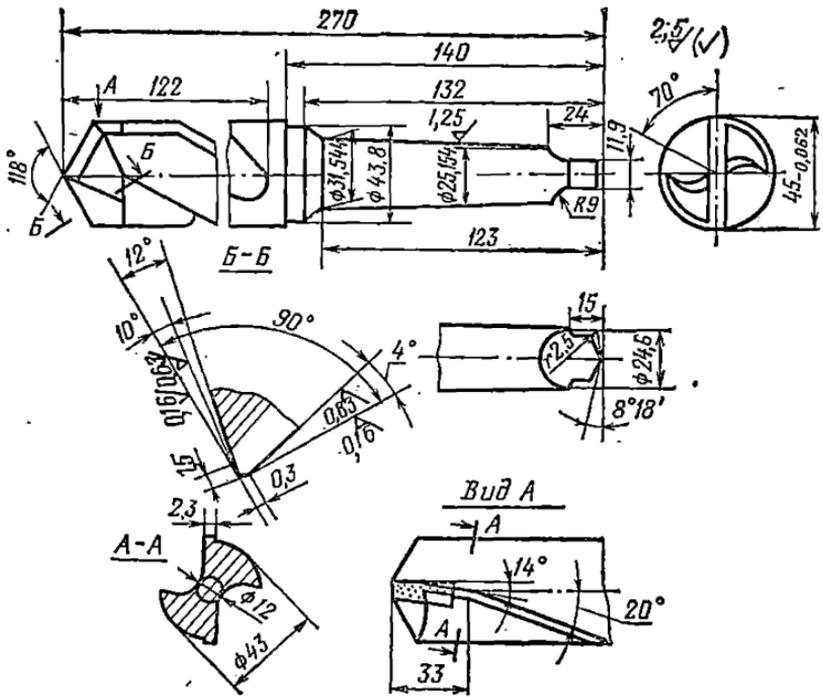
Спиральное сверло с пластинкой твердого сплава.
